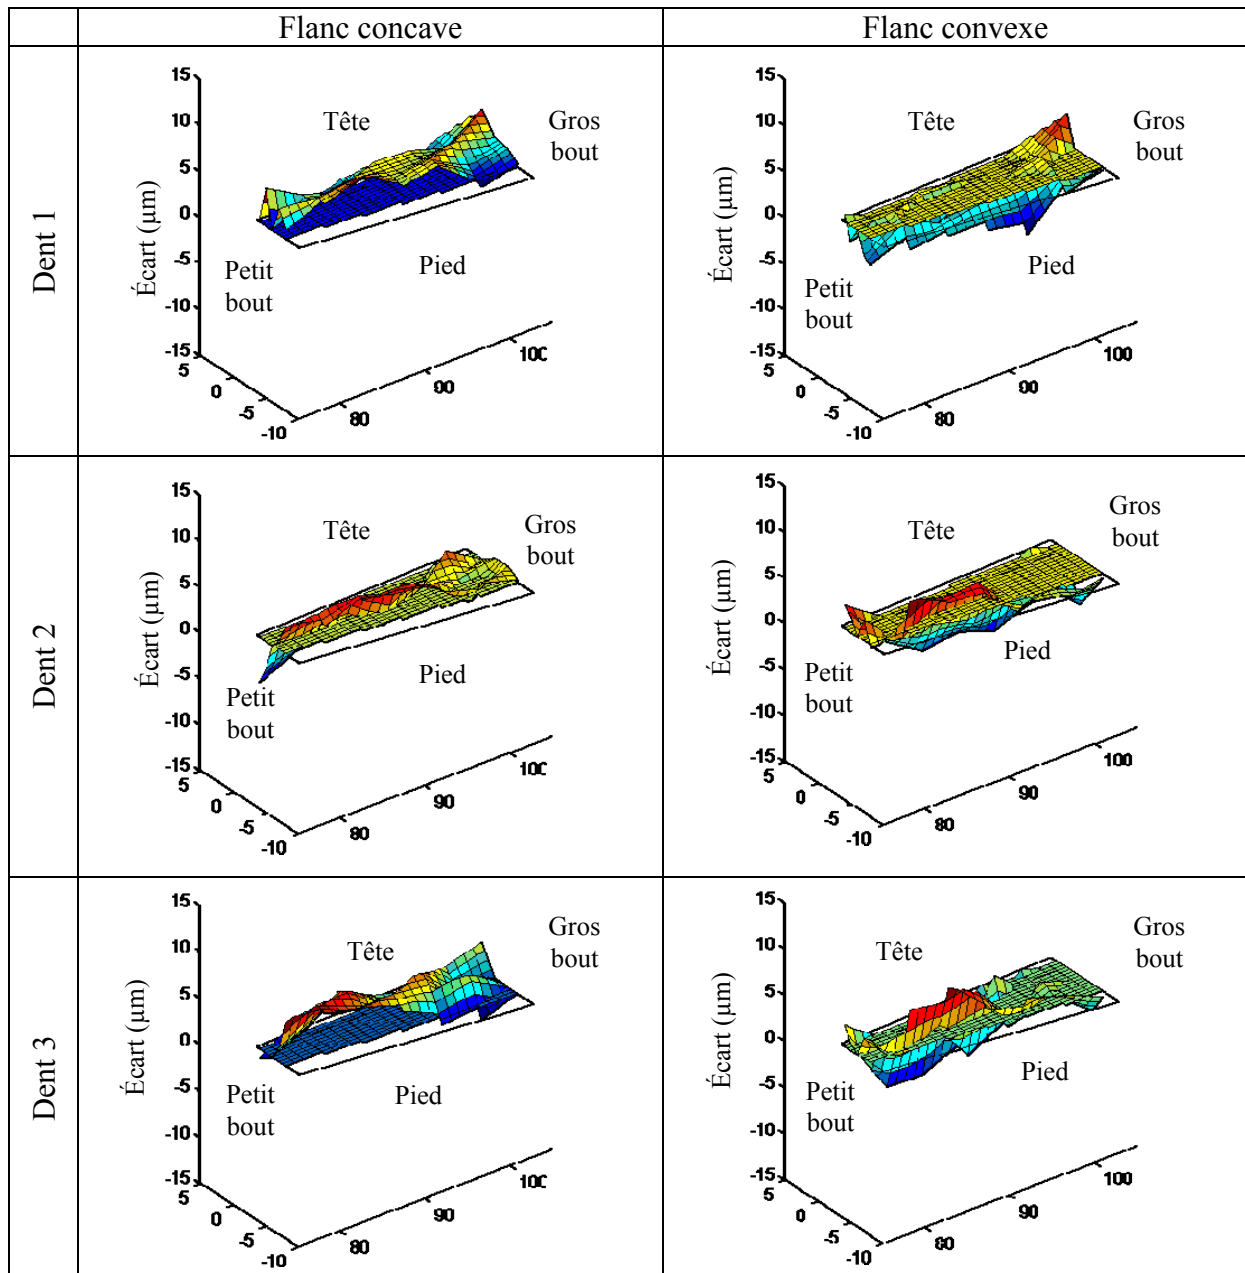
Écarts entre les surfaces des dents usinées et de la CAO pour le cas de la roue Gleason
